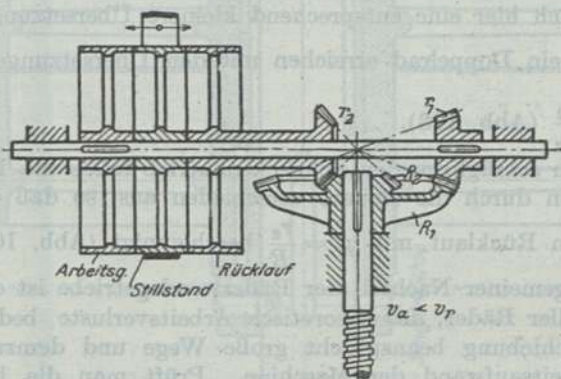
Kegelräderwendegetriebe mit schnellem Rücklauf.
